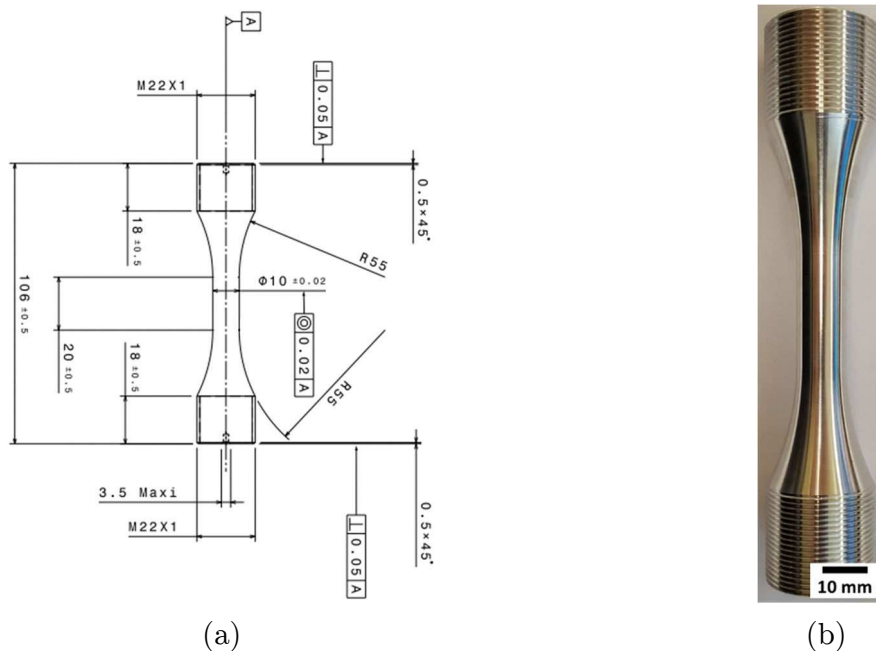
(a) plan de l'éprouvette de fatigue, (b) éprouvette de fatigue usinée
